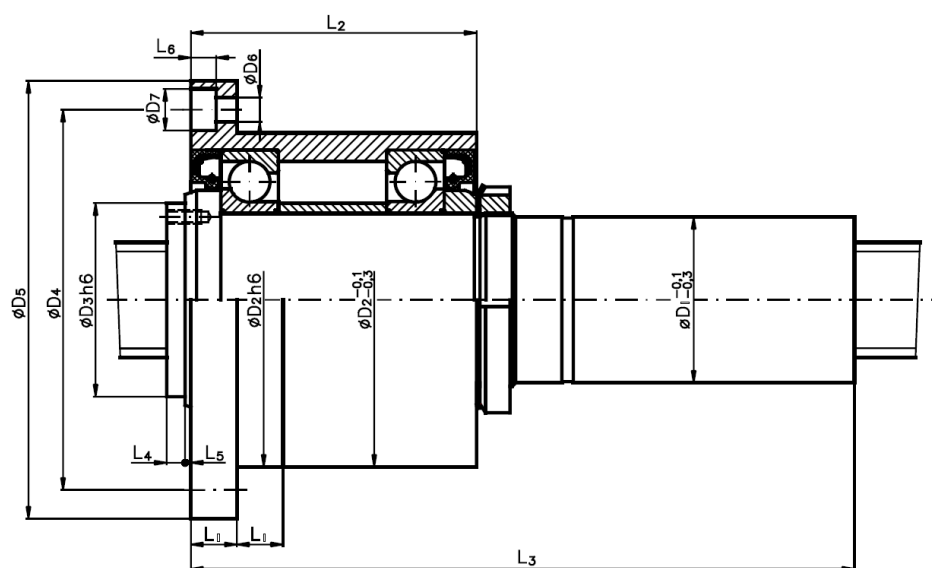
Aplikace KŠM s rotující maticí [Barnes Industries] [26]
